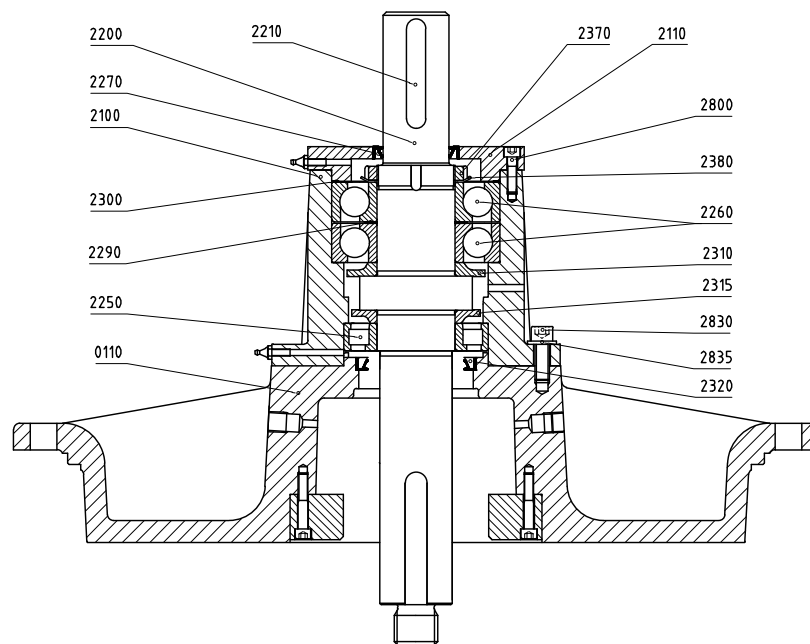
Разборка подшипников 150В–400, 150–500, 200–250, 200–315.
